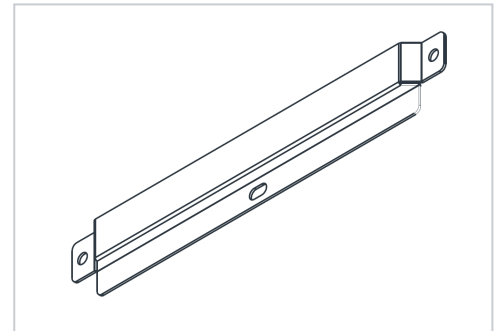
Wandmontageplatte – ausrichten, verschrauben, einhängen
